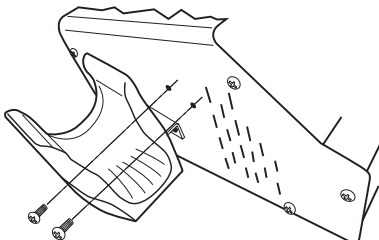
Instalación del soporte del soldador de aire caliente
